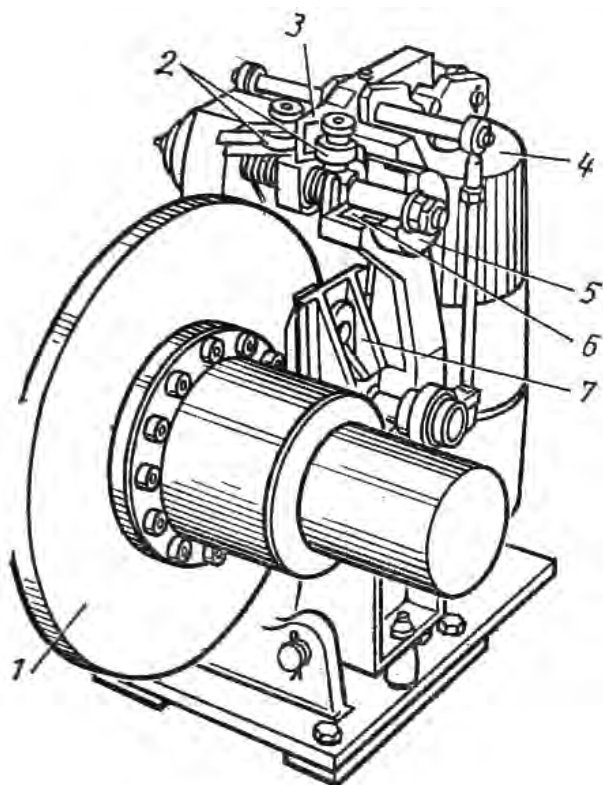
Дисковый тормоз: 1 – тормозной диск; 2 – ролики; 3 – клин; 4 – электрогидравлический толкатель; 5 – тормозные рычаги; 6 – тарельчатые пружины; 7 – тормозные колодки
